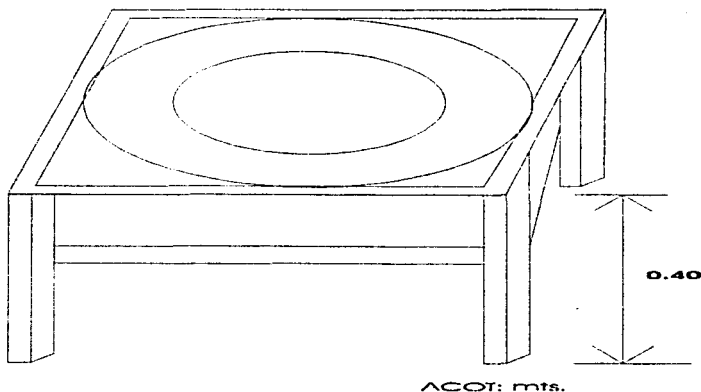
Saladero construido con una llanta cortada por la mitad y sostenida en estructura.
